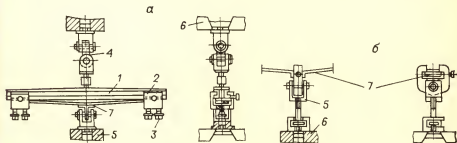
Приспособление для испытания образцов клеевых соединений на неравномерный отрыв (конструкция нижней части меняется в зависимости от образца — варианты а и б): 1 — коромысло; 2 — обойма; 3 — прижимной болт; 4 — шарнирная подвеска; 5 — нижний крепежный узел; 6 — головка испытательной машины; 7 — образцы.
